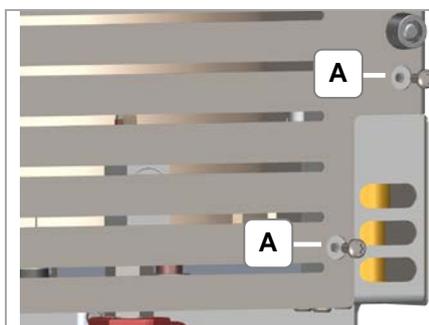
soupape de sécurité, vis, ouvrir le couvercle
